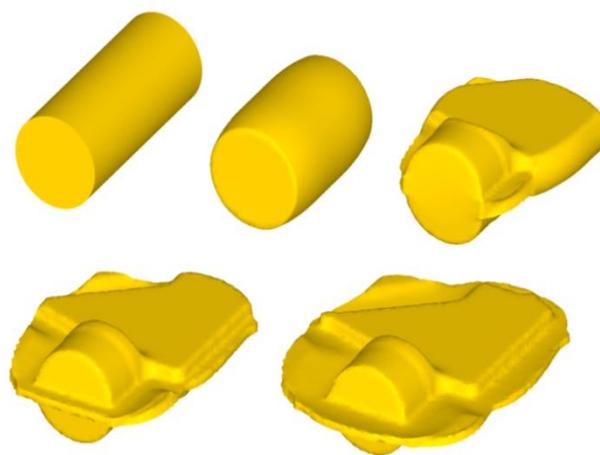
Изменение геометрии заготовки по стадиям процесса горячей объёмной штамповки стальной поковки по предлагаемой технологии
